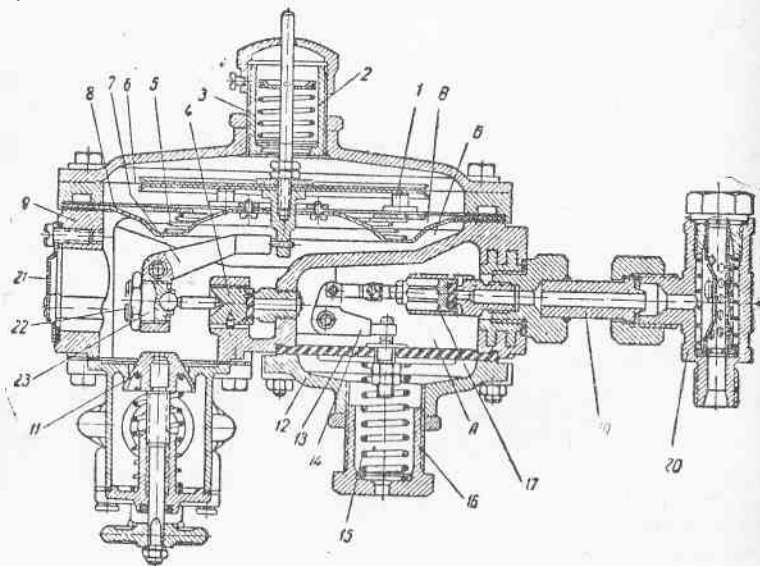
Редуктор МКЗ с винтовым дозатором.
